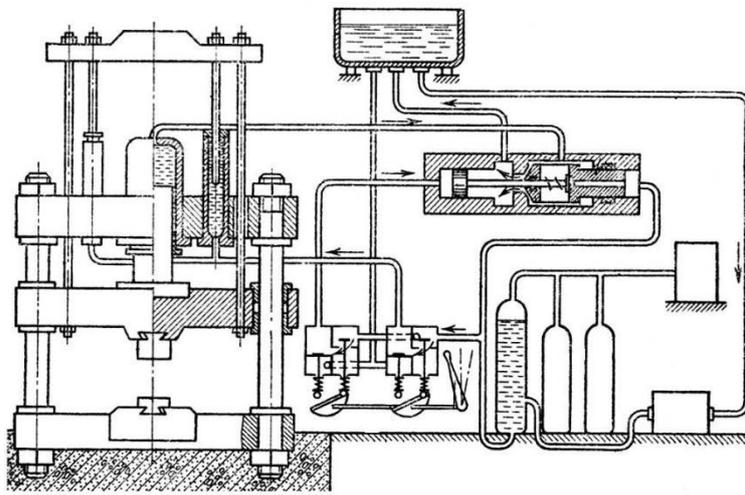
Схема устройства гидравлического ковочного пресса с насосно-аккумуляторным приводом
